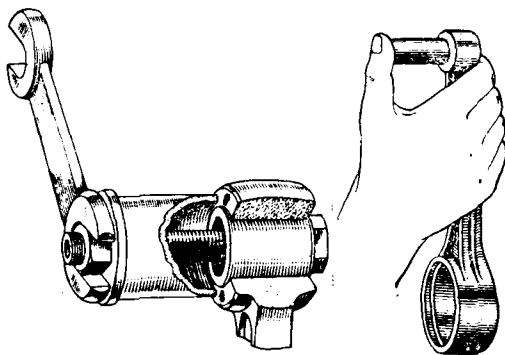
Выпрессовка и проверка втулки малой головки шатуна
